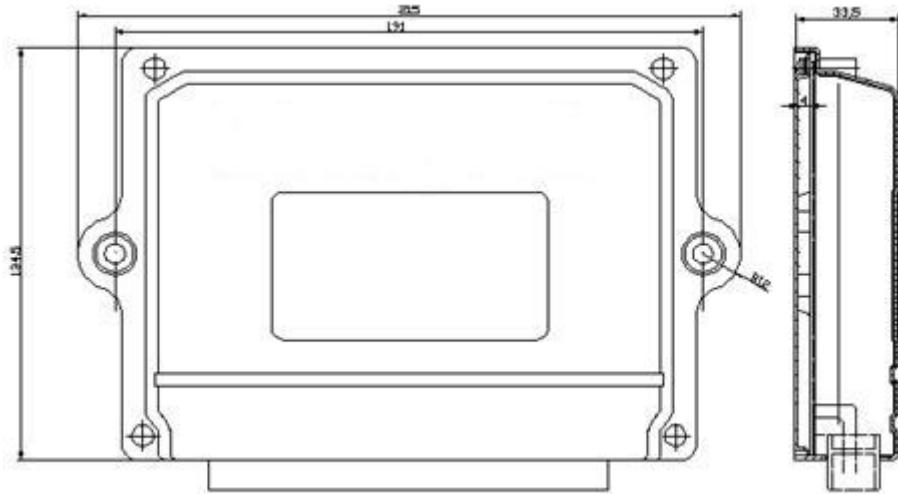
DX201,DX101 安装尺寸/Fig.6-1-1 Installing Dimension of DX201 and DX101
